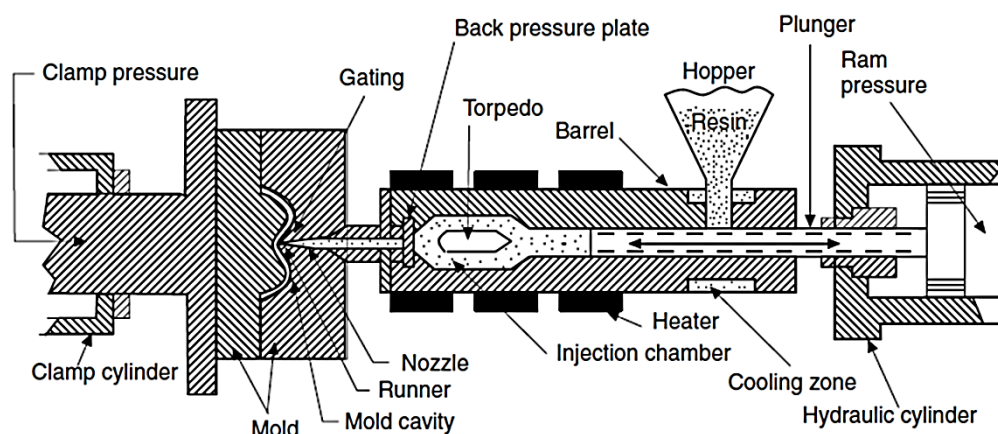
Esquema típico de uma máquina de moldagem por injeção. (Chanda e Roy, 2006)
